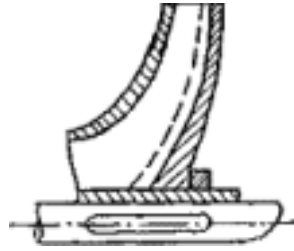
Схема підрізування робочого колеса по ширині
